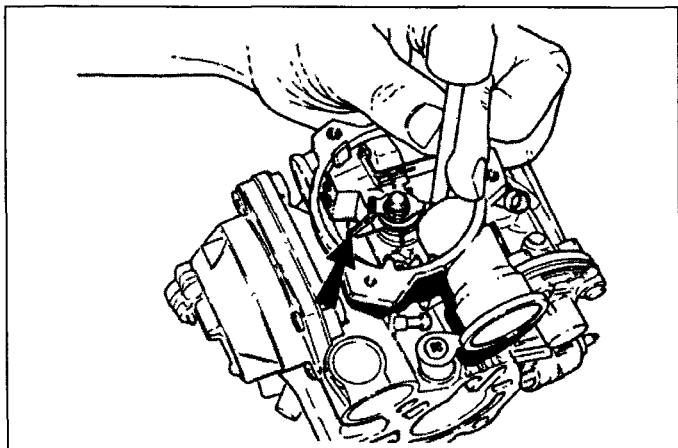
Механизм вакуумного привода "подсоса" и предварительная установка пусковых оборотов
